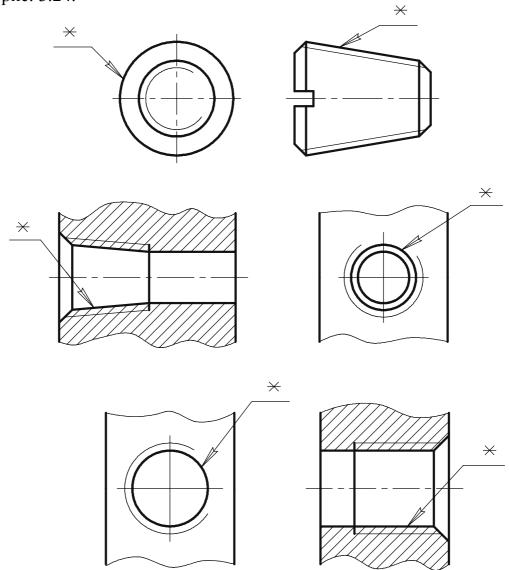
Нанесение обозначений конических резьб и трубной цилиндрической резьбы
